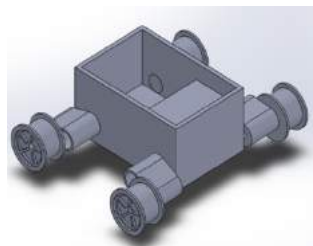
Vista isométrica del diseño de robot sembrador. Fuente: Elaboración propia.
